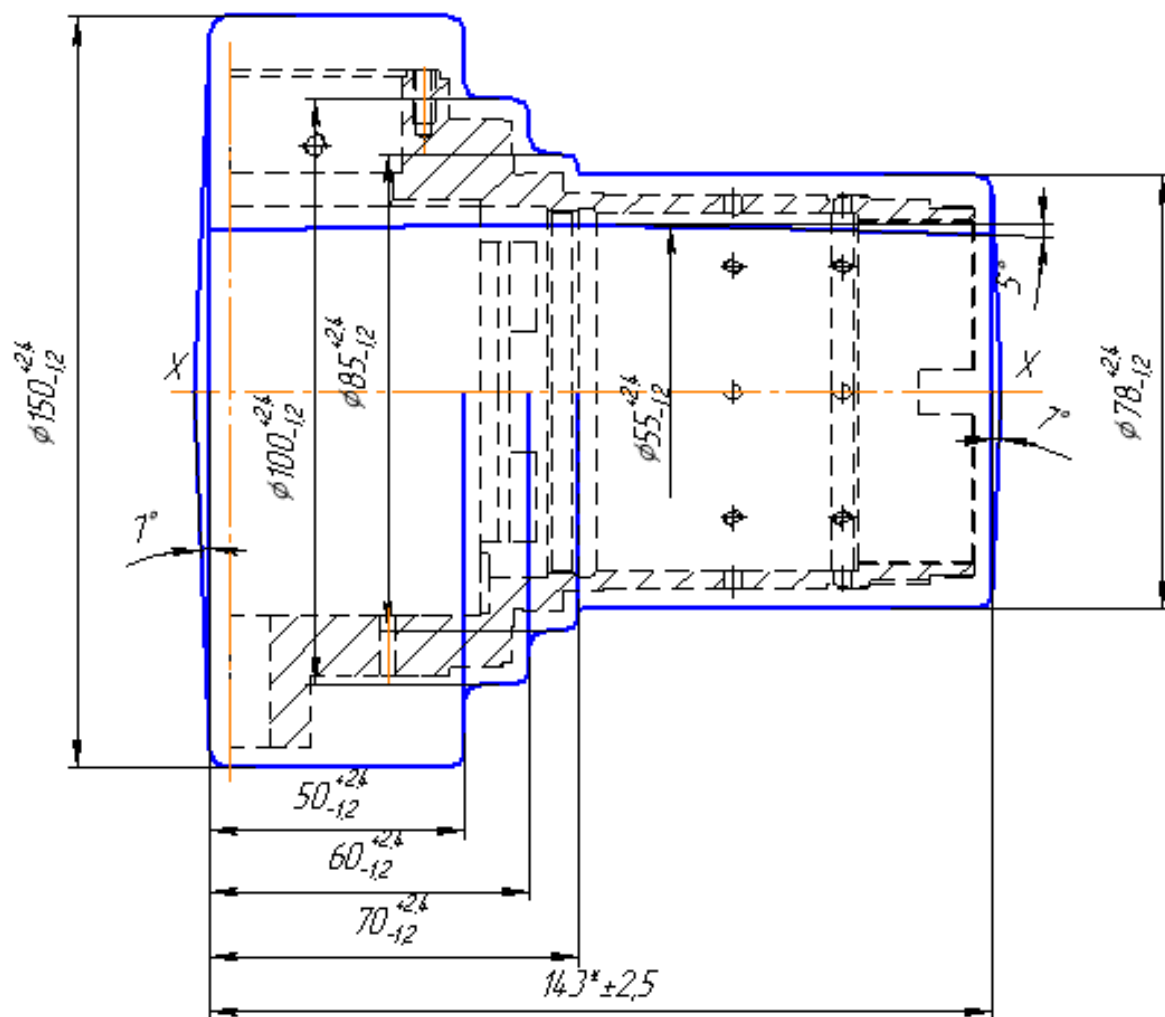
Чертеж заготовки детали «Корпус»
